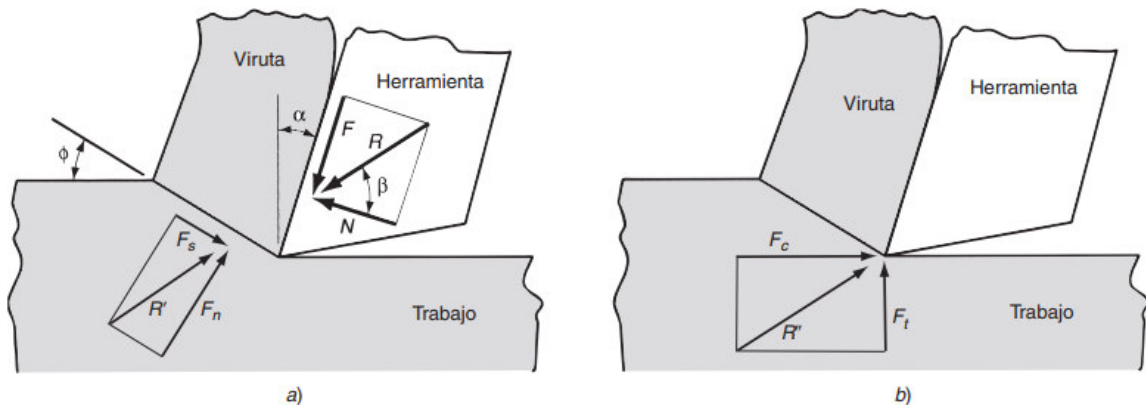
Grupo de fuerzas en el corte ortogonal: a) Fuerzas que actúan sobre la viruta en el corte ortogonal, b) Fuerzas que actúan sobre la herramienta y son medibles.
